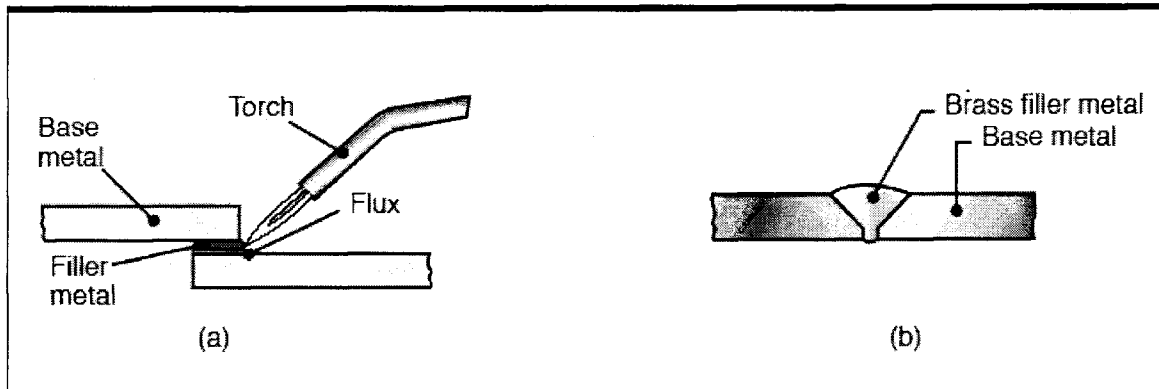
Operaciones para la soldadura. "Brazing"
